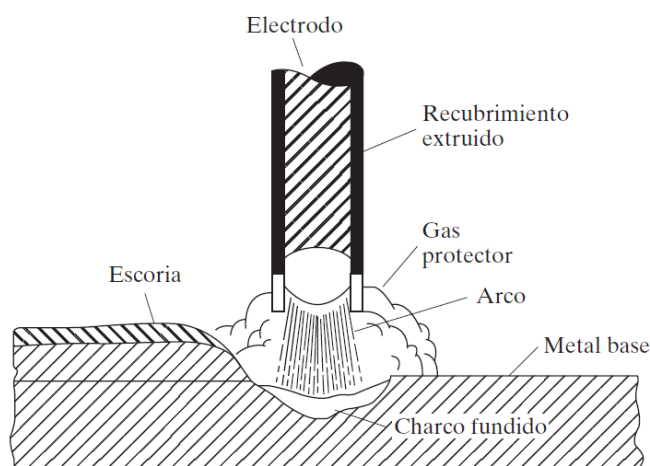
Elementos del proceso de soldadura SMAW
